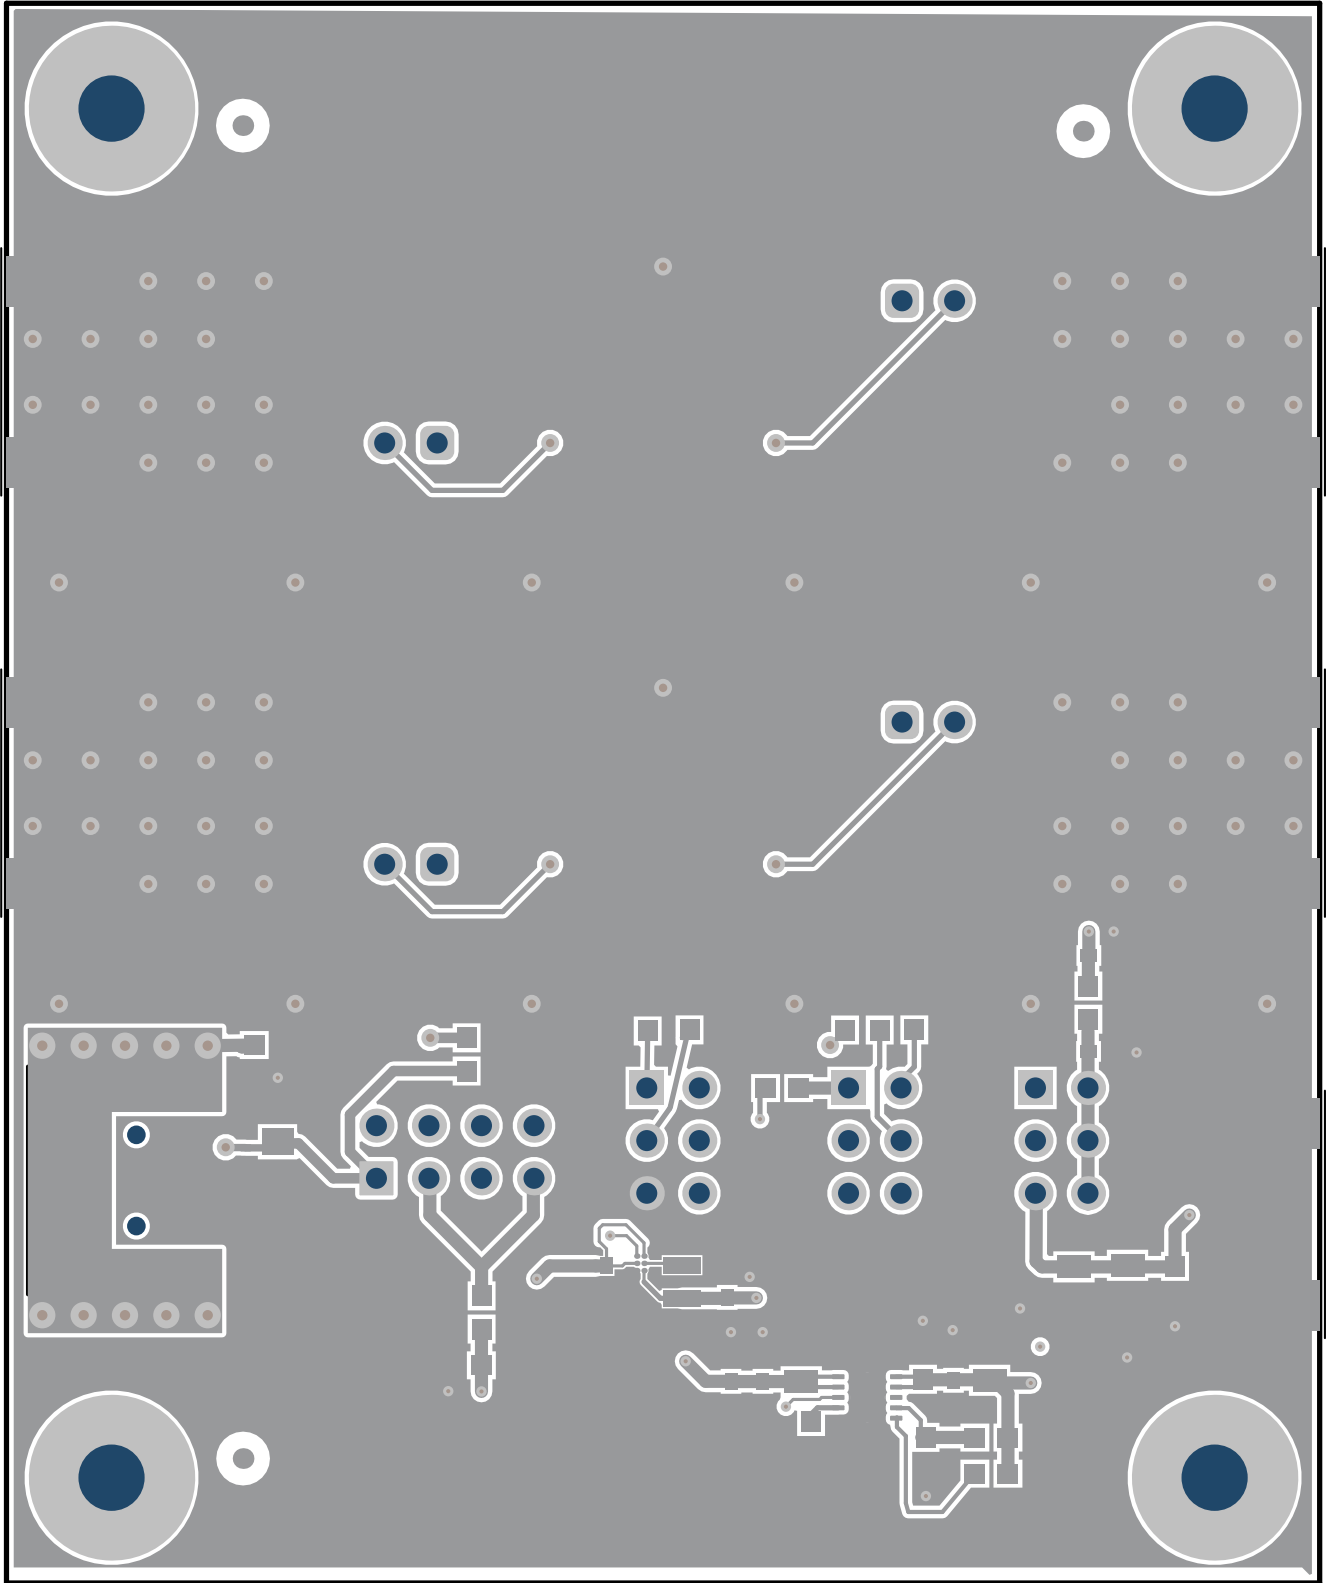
CDC6 EVM 的 PCB 布局示例 - 底层
